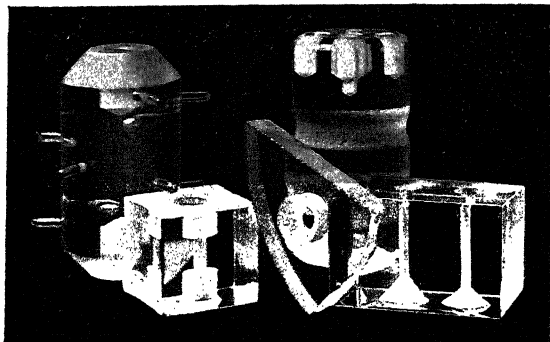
Verschiedenartige Bohrungen an Glaskörpern mit Widiawerkzeugen.
